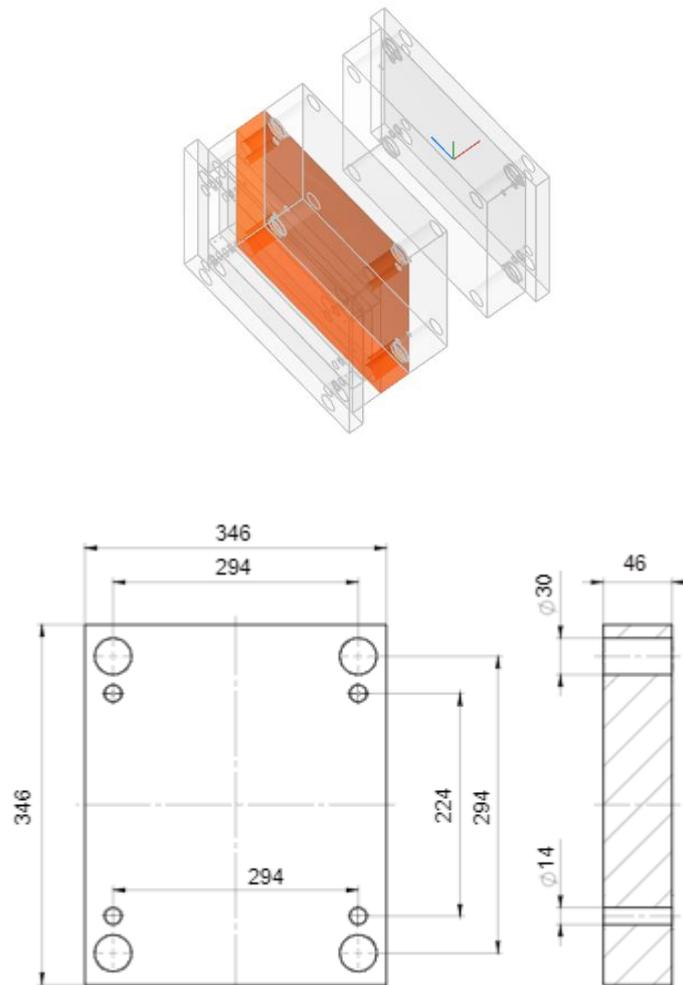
Dimensiones de la placa intermedia, HASCO.
